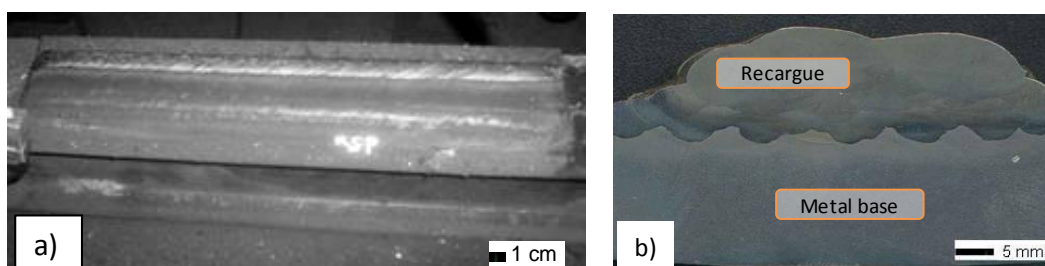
a) Probeta soldada, b) Corte transversal de la probeta soldada.
